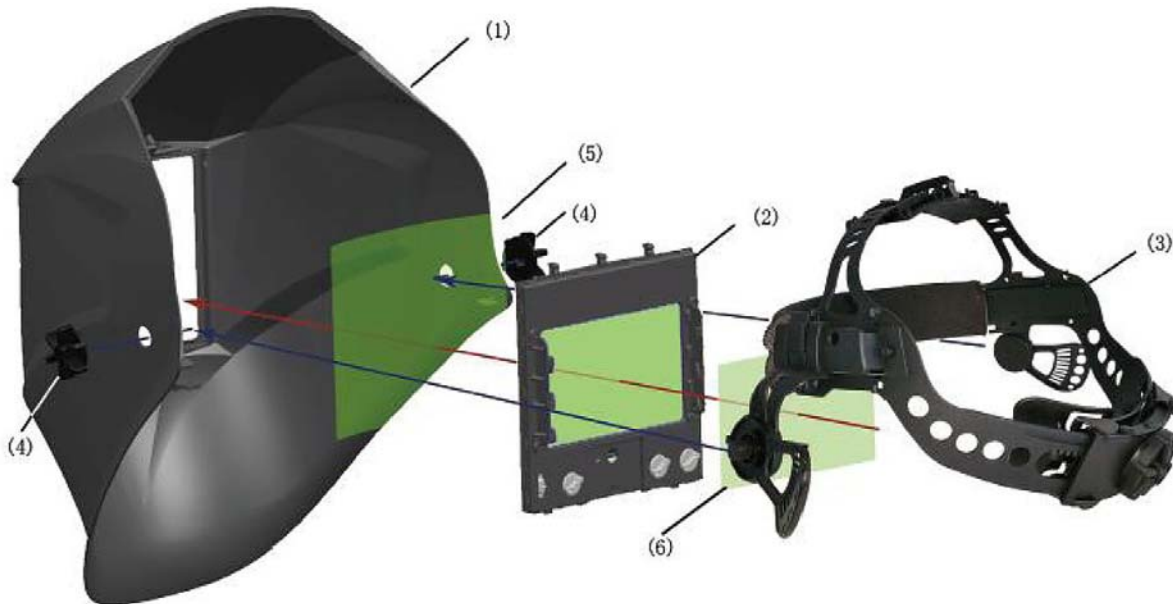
Ersatzteilzeichnung 1 / Spare parts drawing 1
